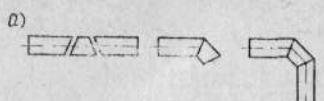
Схема изготовления сварных деталей трубопроводов
